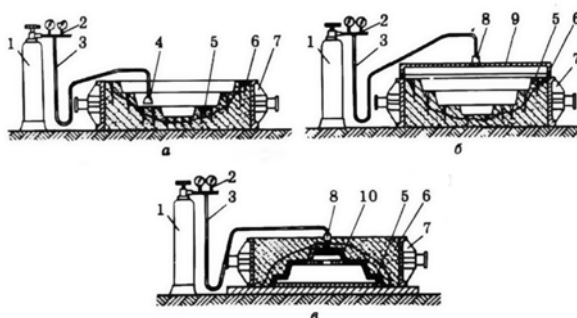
Способы продувки формы углекислым газом: 1 — балло с углекислым газом; 2 — редуктор; 3 — шланг; 4 — сопло; 5 — облицовочная жидкостекольная смесь; 6 — наполнительная смесь; 7 — опока; 8 — ниппель; 9 — зонт; 10 — модель.
